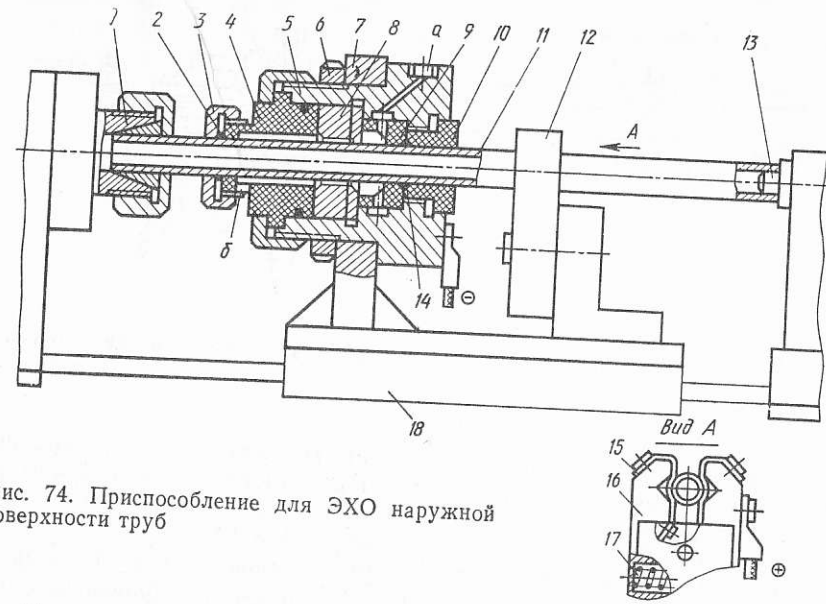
Приспособление для ЭХО наружной поверхности труб
